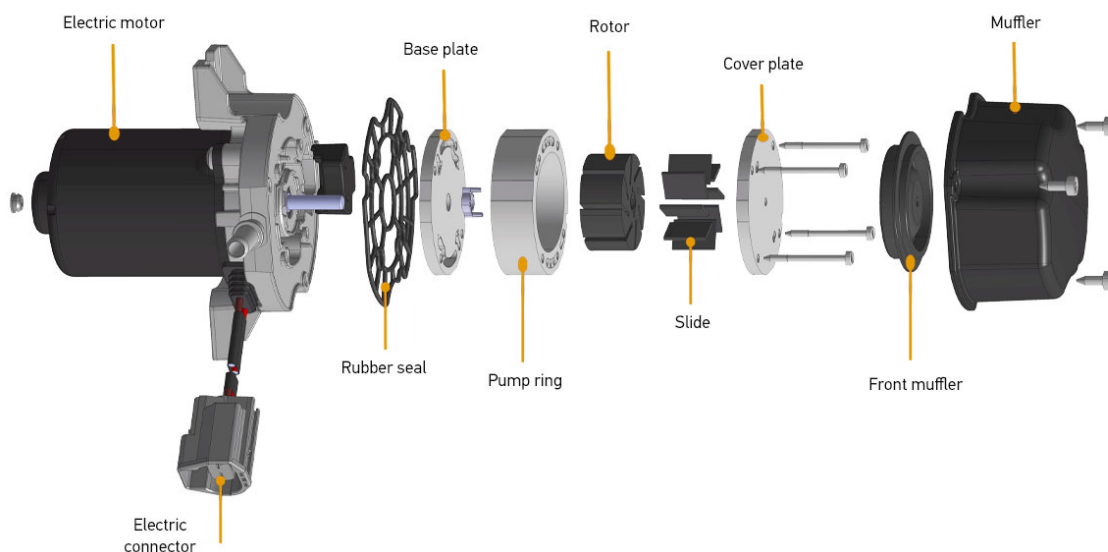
Bomba de vácuo vista explodida.HELLA (2023)
